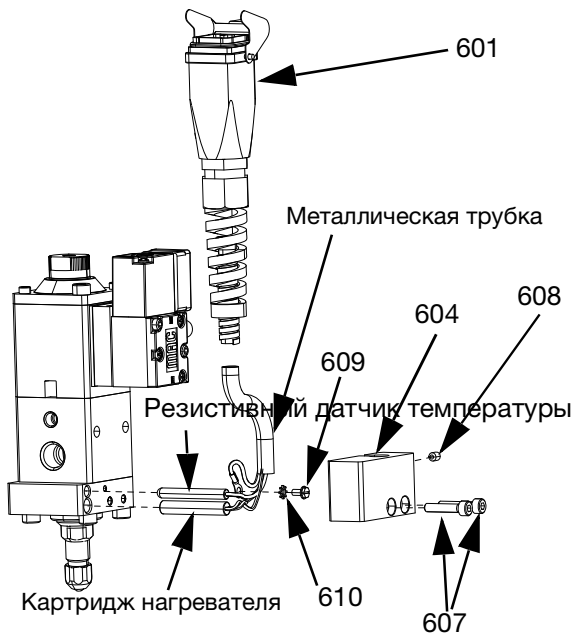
Нагреватель в сборе для выпускного блока 0 мм
